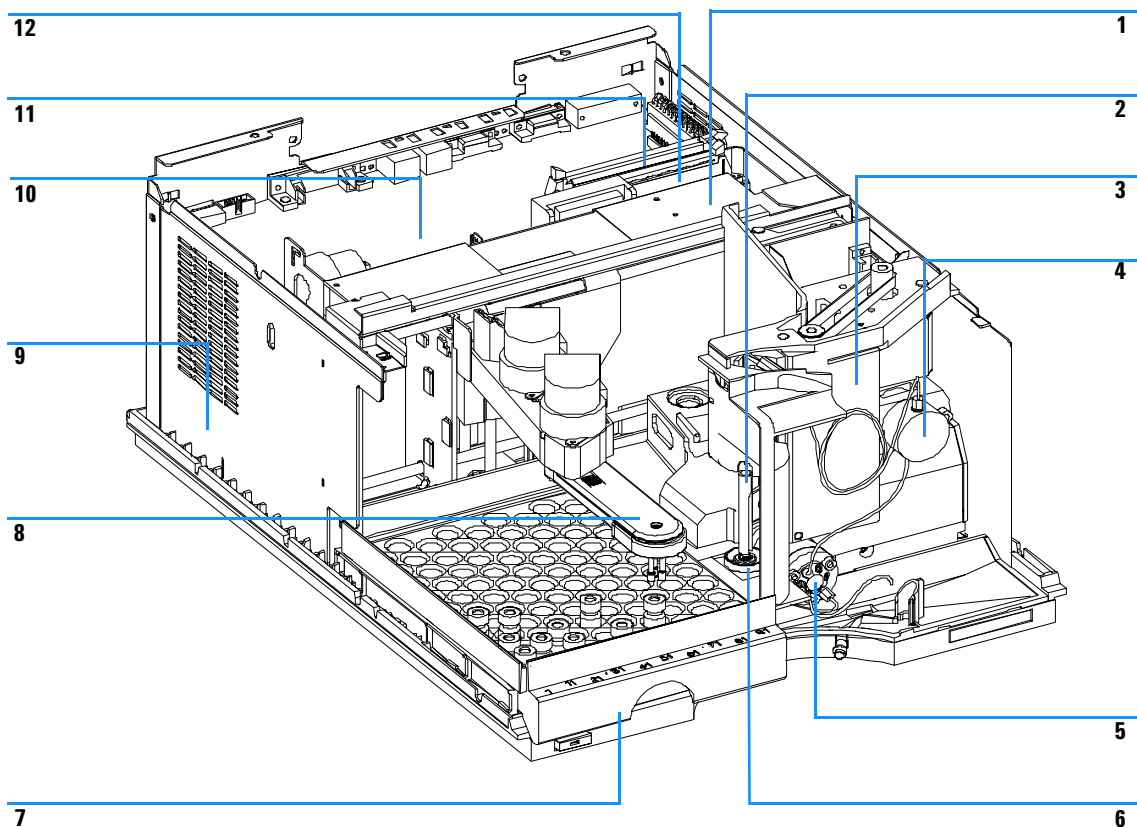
Mikro-Wellplate-Probengeber - Gehäuseteile
